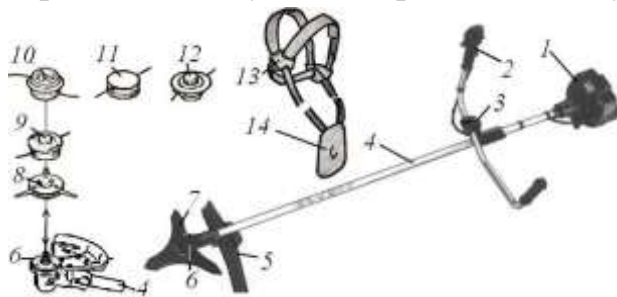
Моторная коса: 1 – двигатель; 2 – рукоятка управления; 3 – кронштейн крепления рукоятки; 4 – штанга с валом; 5 – защитный кожух; 6 – редуктор; 7 – трехножевой режущий орган; 8 – трехножевая пластмассовая косильная лопасть; 9,10 – полуавтоматические двухнитевые головки; 11,12 – двухнитевые головки ручной настройки; 13 – лямка; 14 – карабин
